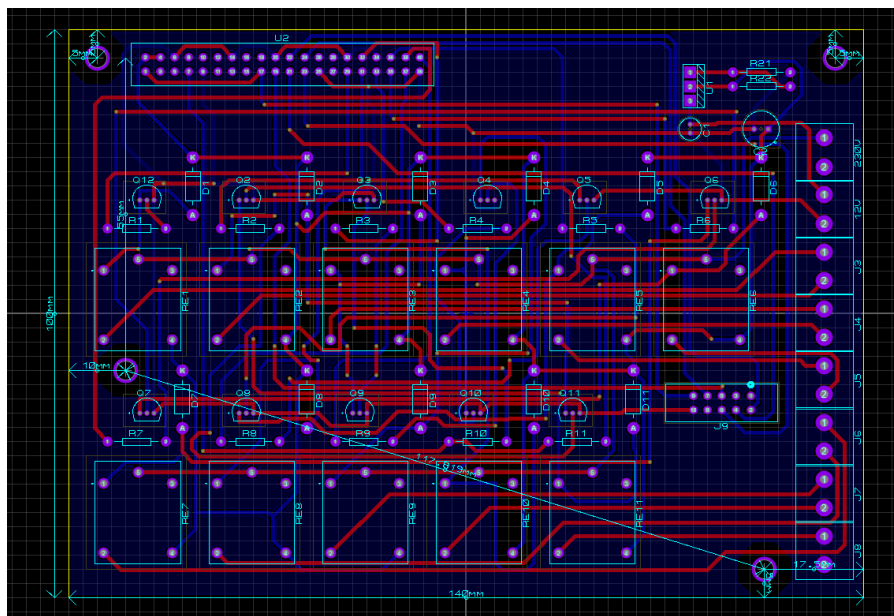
Obtenção das dimensões da PCB e da respetiva furação.
